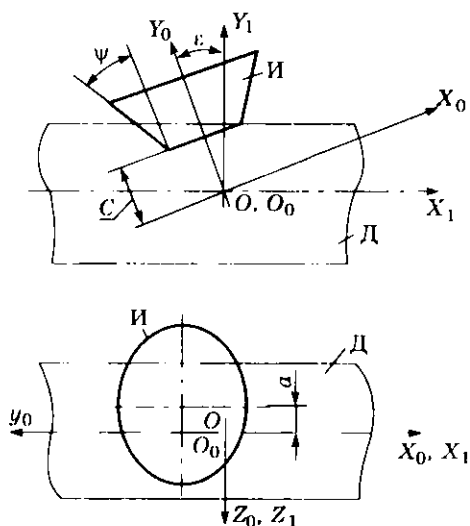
Схема фрезерования винтовой канавки угловой фрезой
